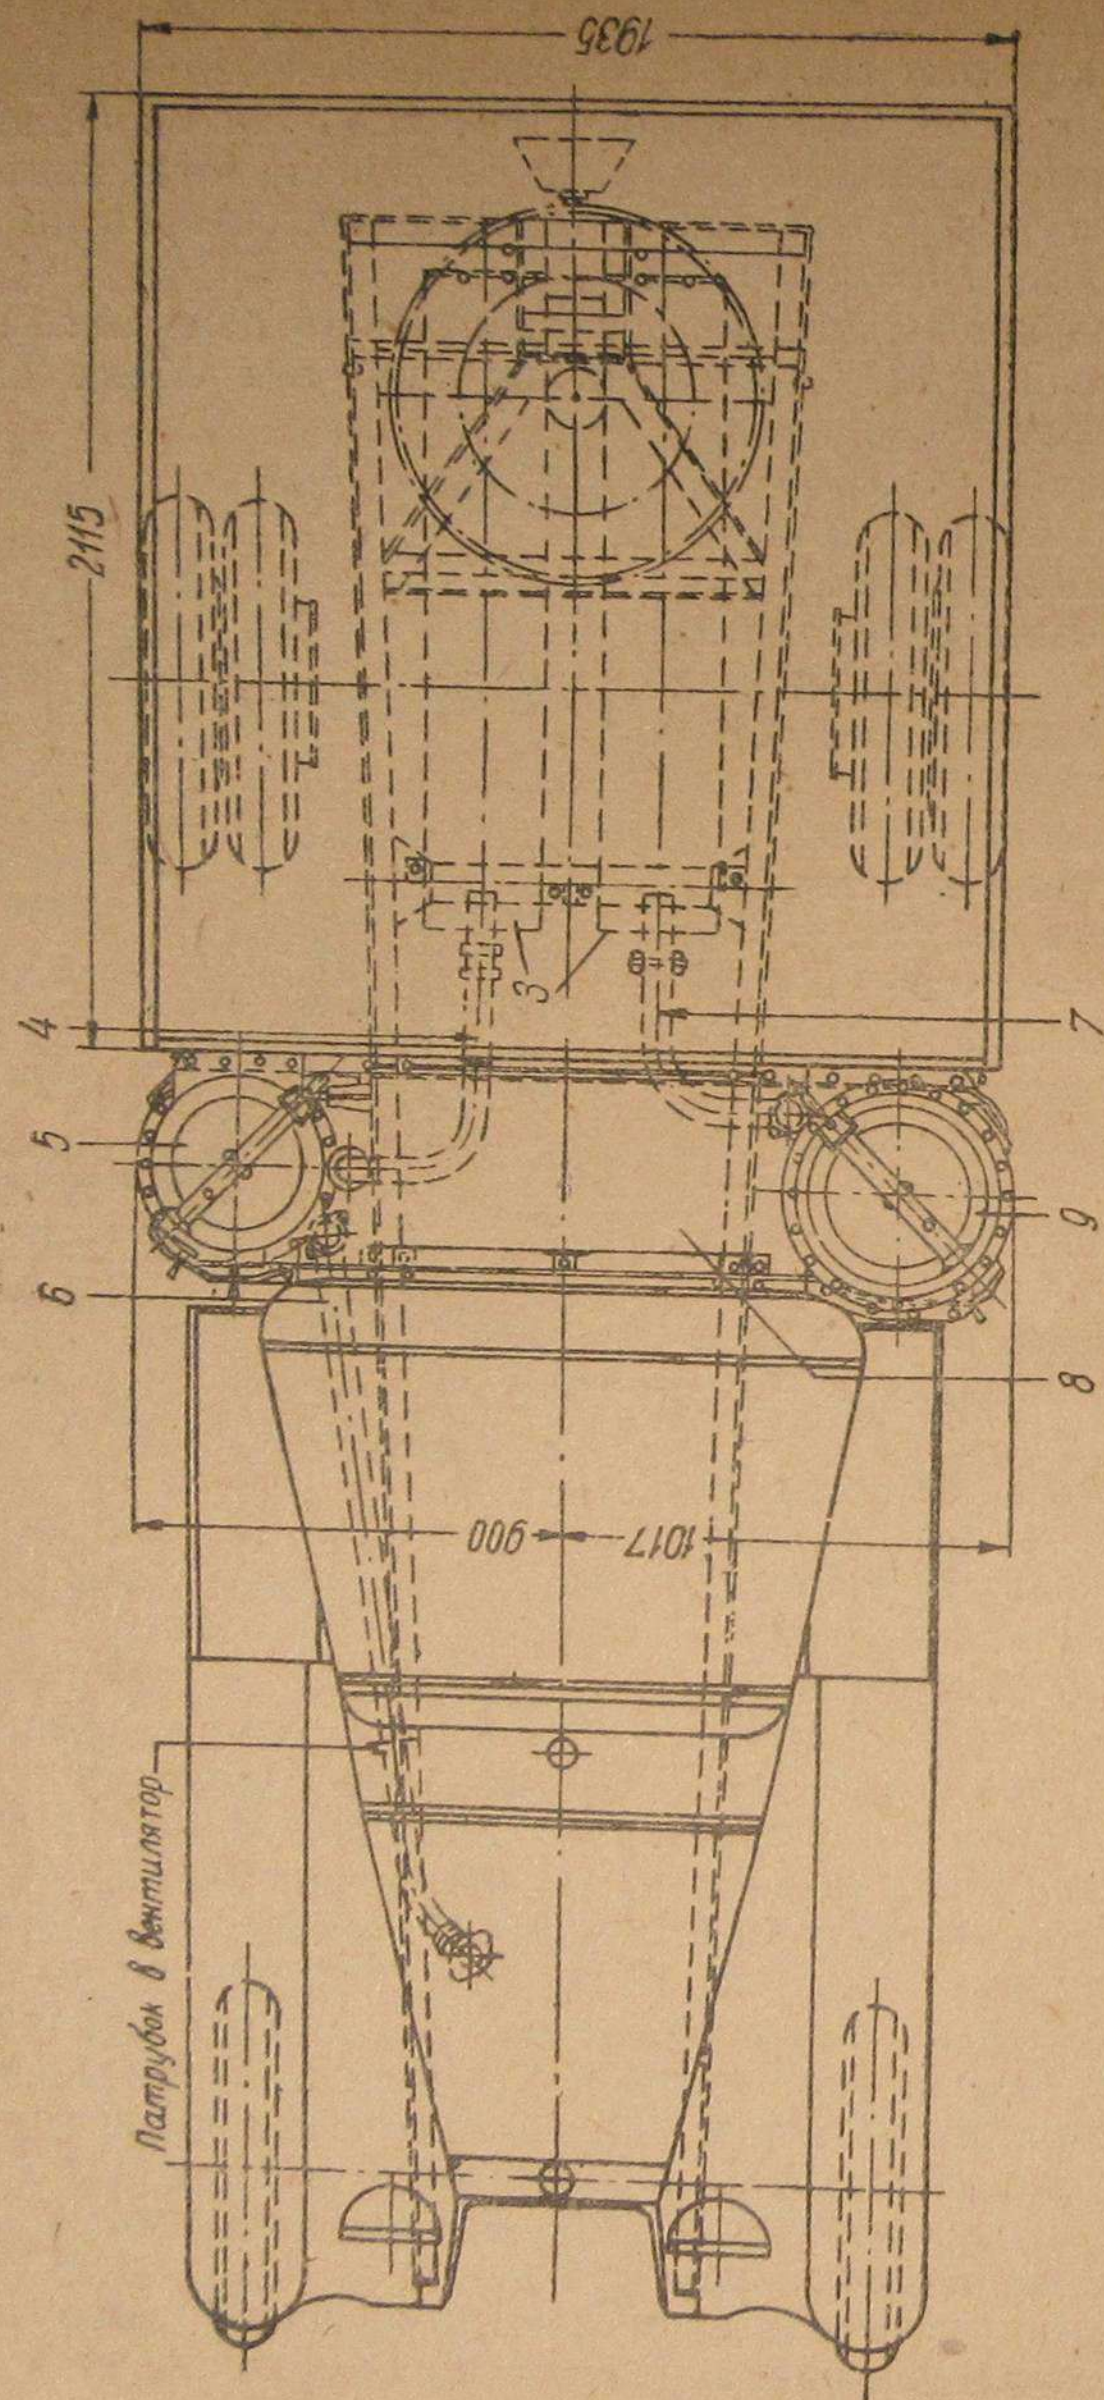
Схема расположения газогенератора на автомобиле (вид сверху)
